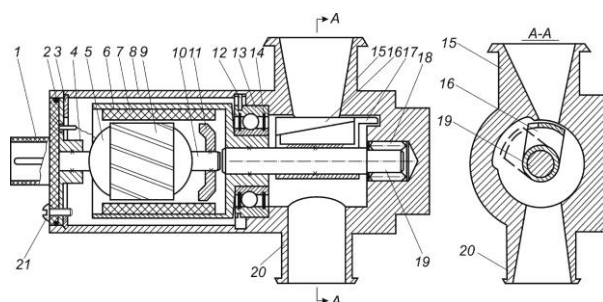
Повздовжній і поперечний вигляд електромагнітного регулятора подачі газу для дизеля з насос-форсунками механічного типу:
